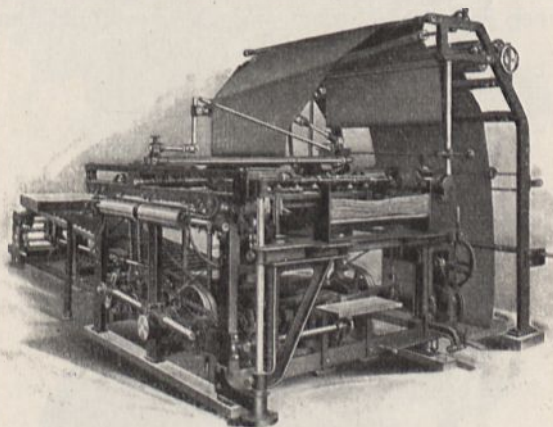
Doublier-Einspänmaschine. (Roßweiner Maschinenfabrik A.-G.)
